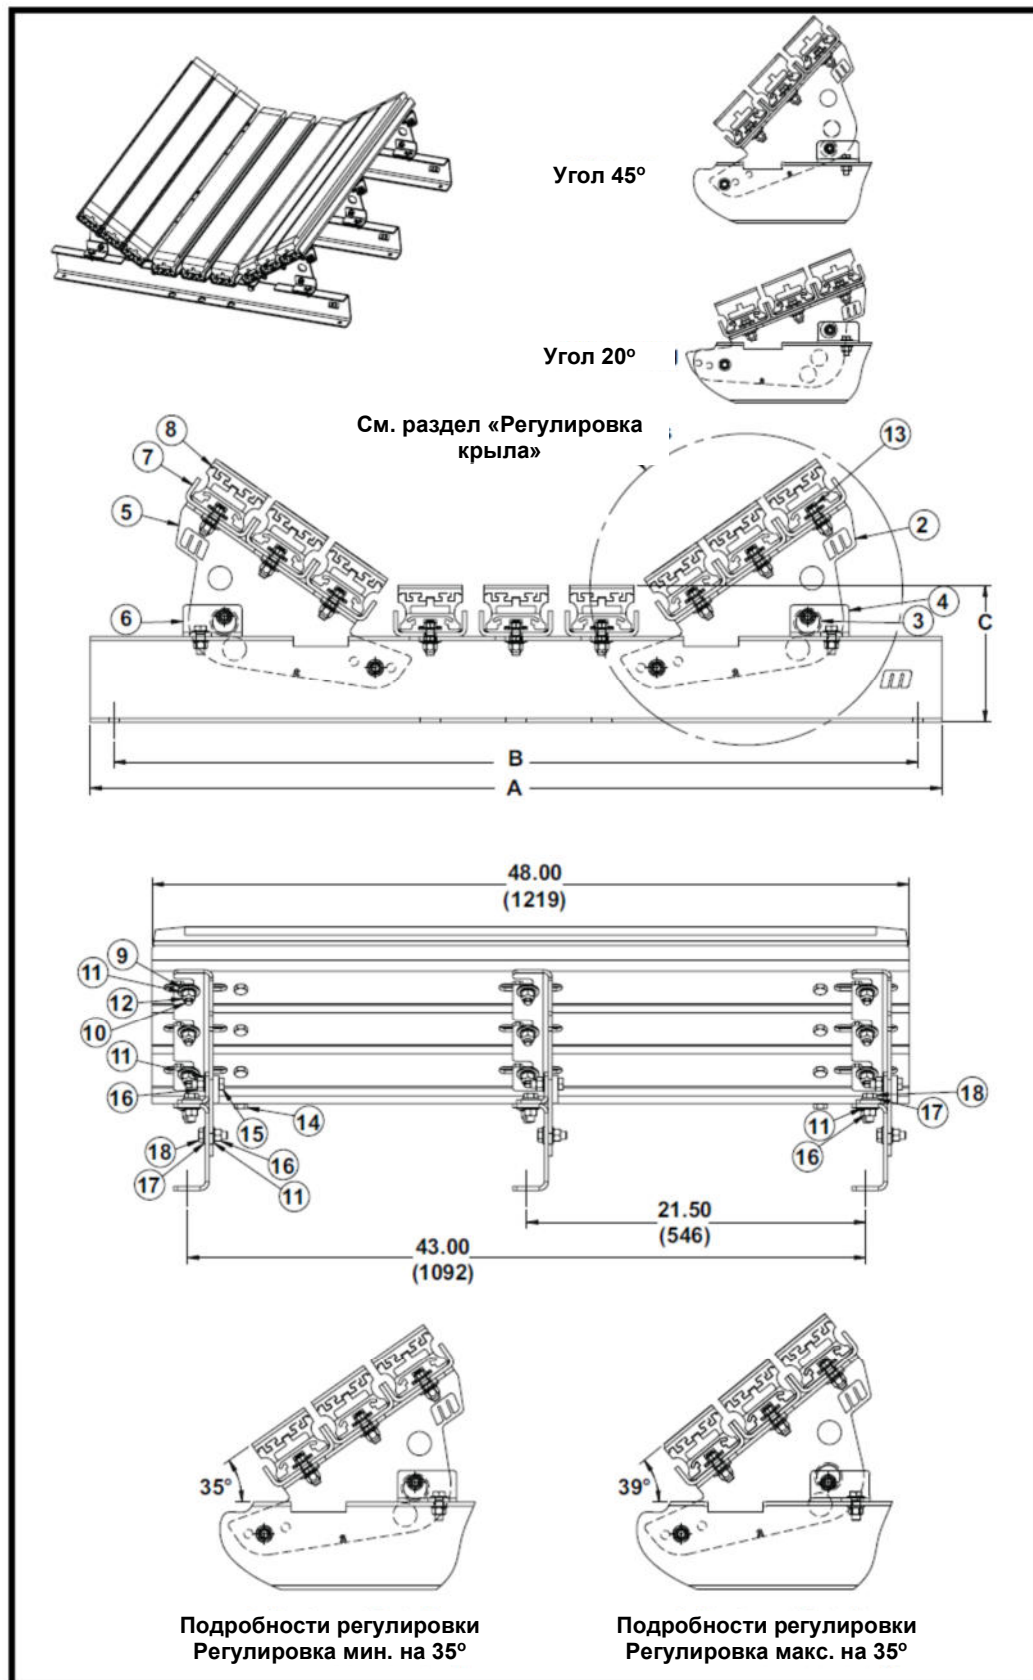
Противоударная опора Martin® LD в сборе, Н/Д 36010-XXX (Лист 1 из 2)
